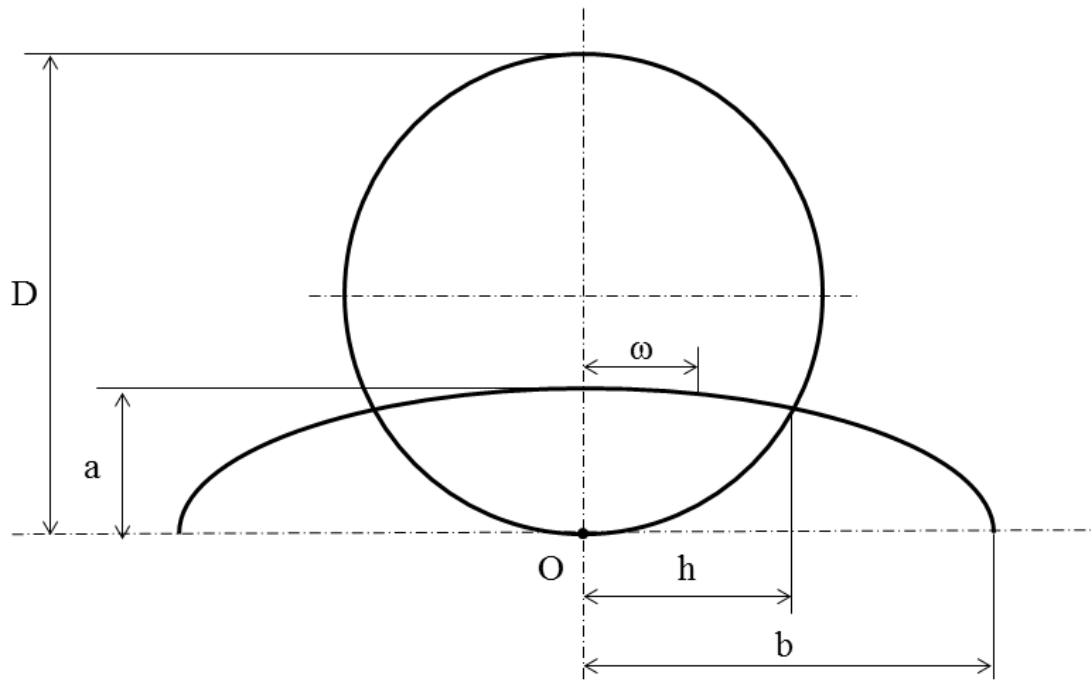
Sección transversal de la zona fisurada de un eje y parámetros característicos de una fisura semielíptica con forma convexa
